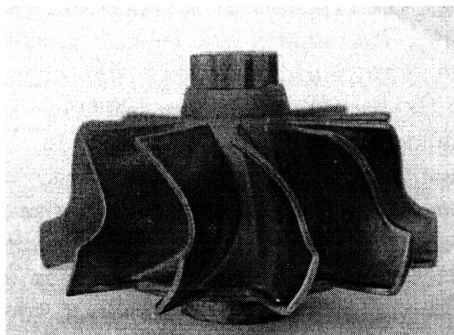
Внешний вид лопатки автотурбокомпрессора
